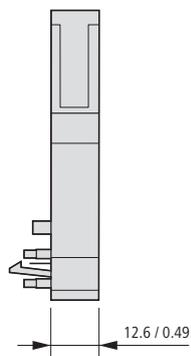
Rückansicht BL20-Modul komplett in Scheibenausführung
